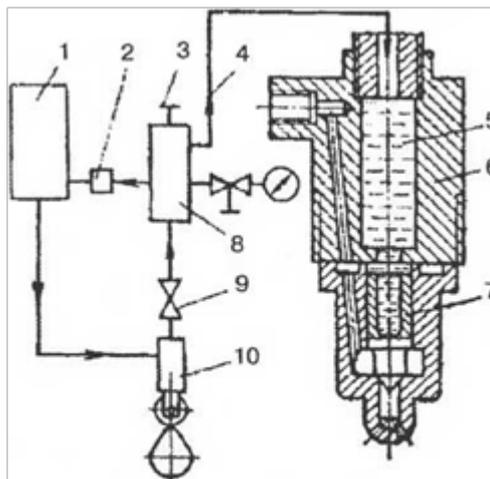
Схема установки форсунки с гидравлическим погружением иглы: 1 – бак; 2 – перепускной клапан; 3 – предохранительный клапан; 4 – трубопровод; 5 – полость; 6 – корпус форсунки; 7 – игла; 8 – аккумуляющая емкость; 9 – обратный клапан; 10 – насос
